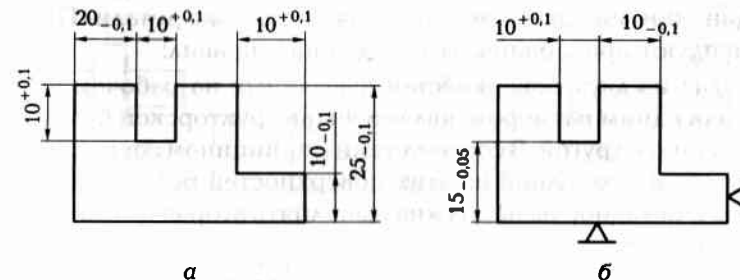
Чертеж детали (а) и схема базирования заготовки (б)
